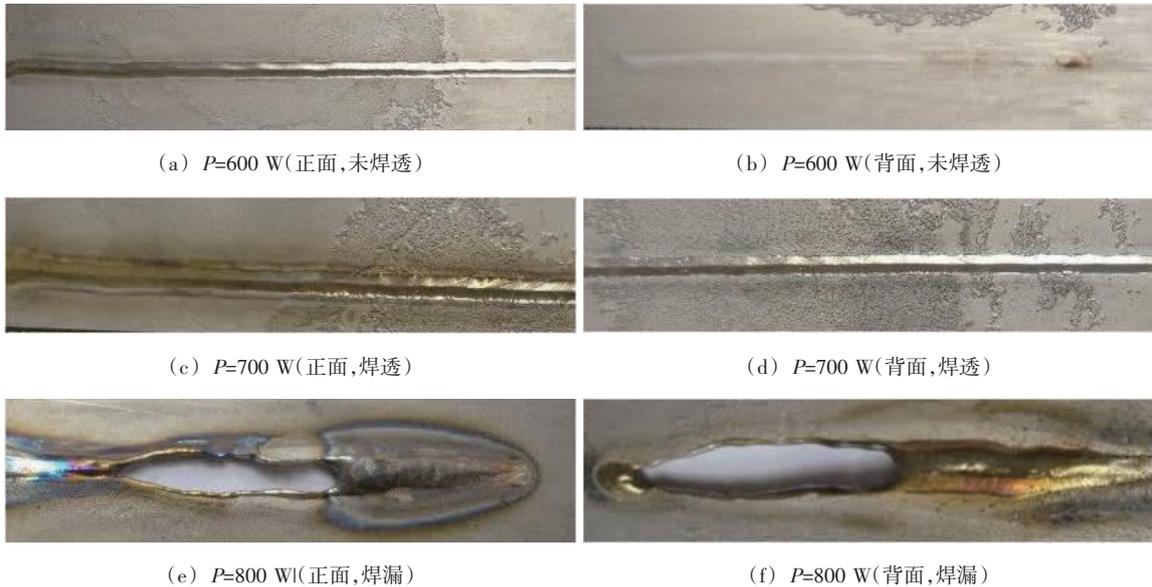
焊接速度3 m/min时激光功率(P)对焊缝成形的影响
